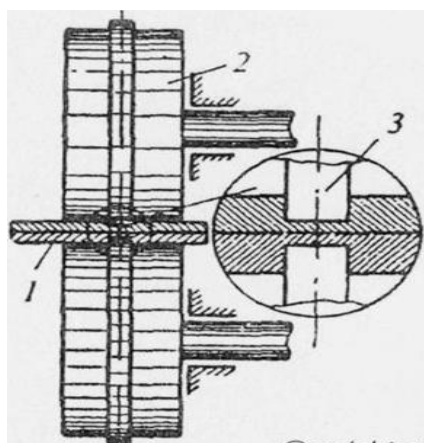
Схема шовной холодной сваркой:
